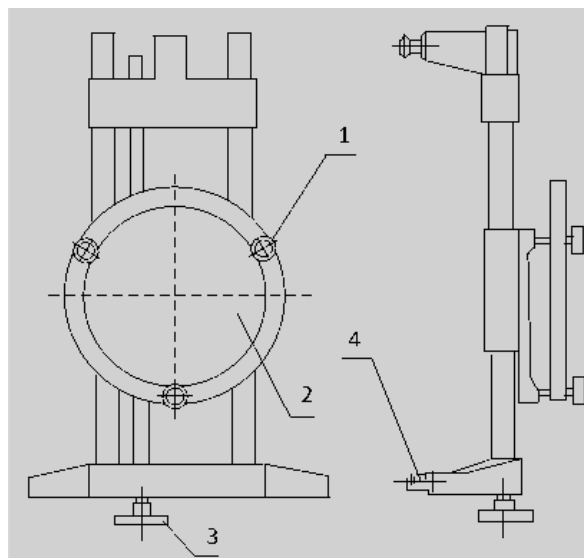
Розпірна консоль колісного блоку: 1 – дзеркала; 2 – регулювальна гайка; 3 – ручка ходового гвинта; 4 – упорний гвинт
